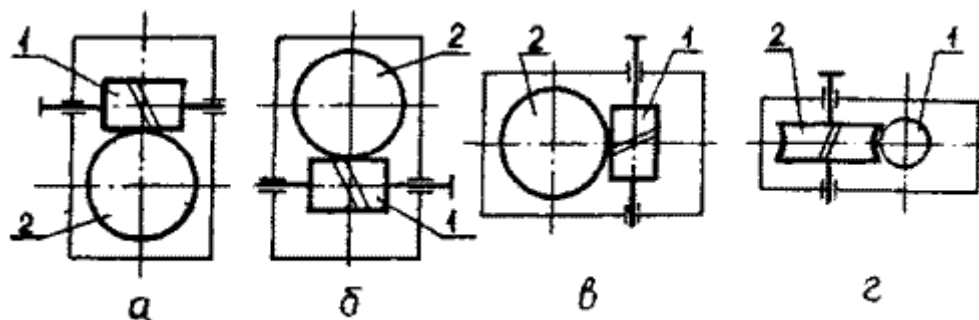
Варианты расположения червяка 1 и червячного колеса 2.
